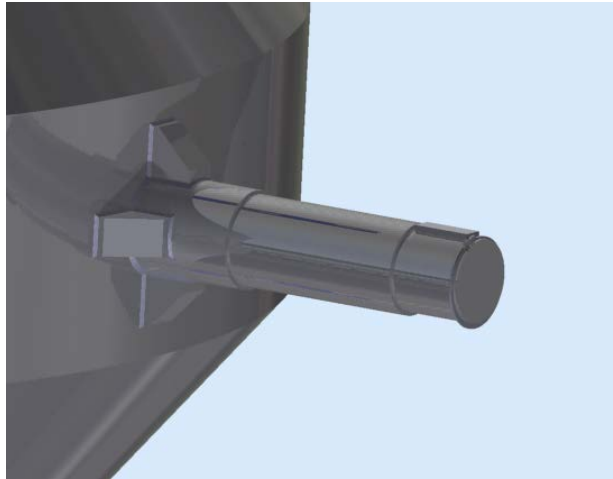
Suport dret soldat. Eix instal·lat al rodament flotant sobre el suport motriu. Es pot observar la xaveta i l'anell de retenció que serviran de fixació per al plat motriu.
